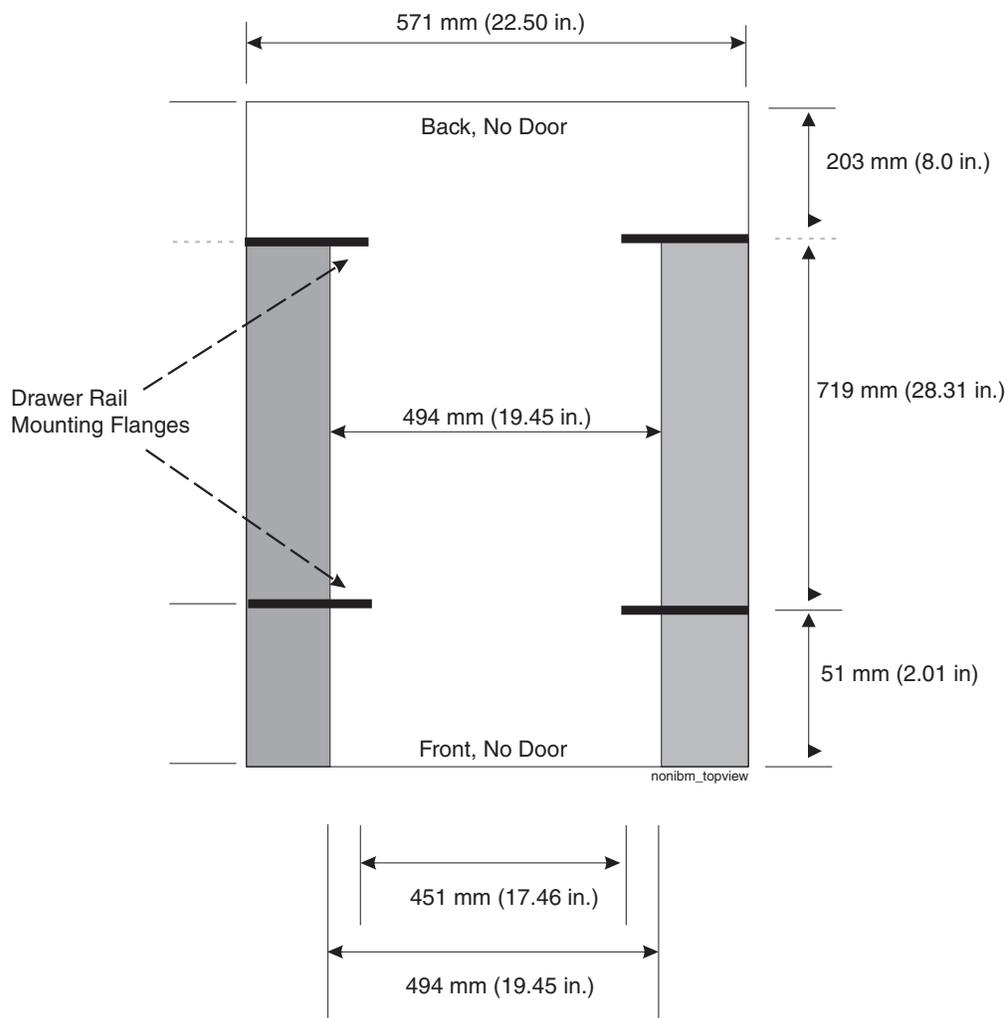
Vista Superior das Dimensões de Especificações de Rack não IBM
